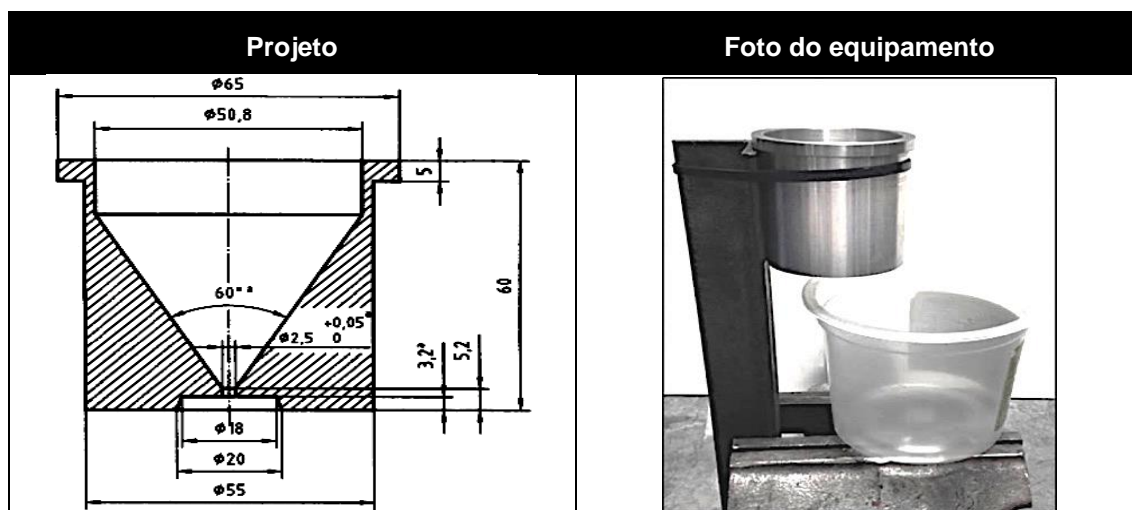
Dimensões do funil Hall e imagem do funil usinado. (74) e foto
